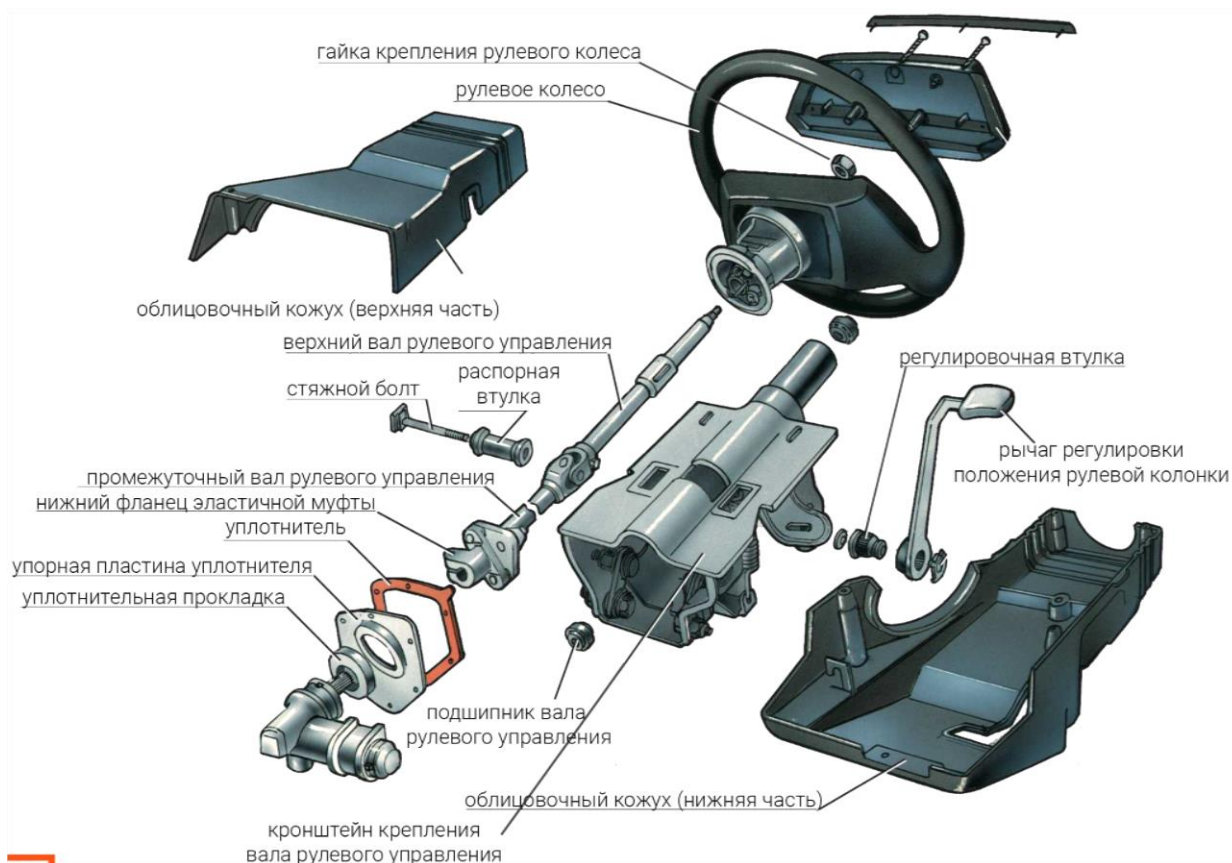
Рулевой механизм автомобиля Lada Vesta
